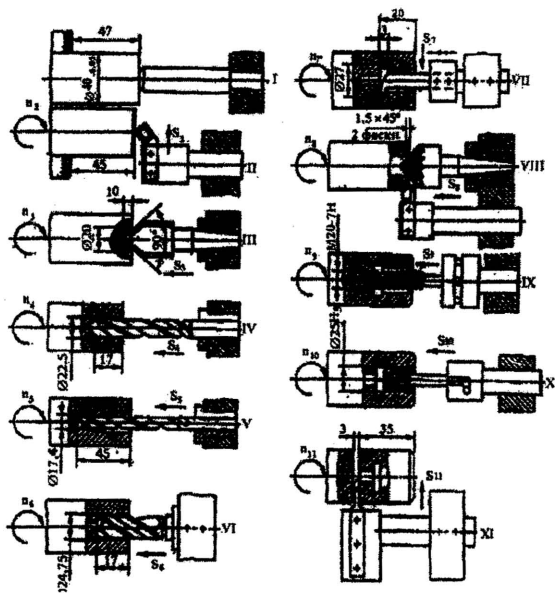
Наладка токарно-револьверного станка мод. 1Г340П
